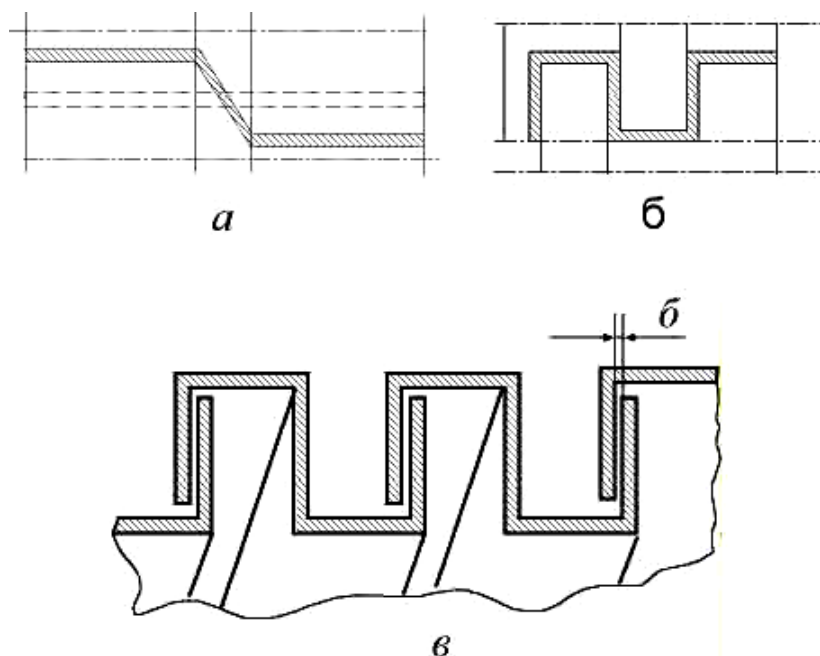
Схема изготовления заготовки металлорукава: а – в первой клети непрерывного стана; б – во второй клети; в – в третьей клети
